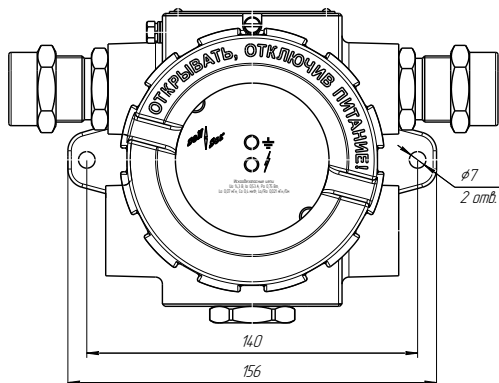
Установочные размеры ВУУК-БП-УЗА-220В
